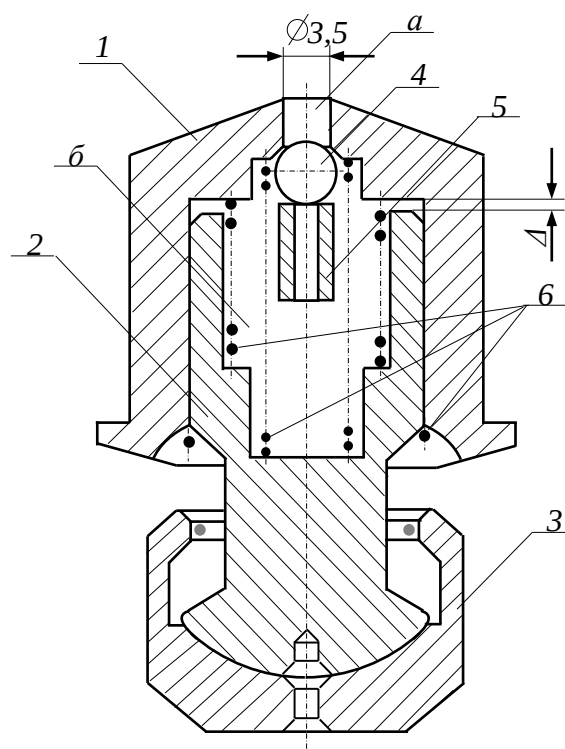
Гідроштовхач механізму газорозподілу ЕУТ Д49: 1 - втулка; 2 – штовхач; 3 – ковпачок; 4 – кульковий клапан; 5 – упор; 6 – пружини
